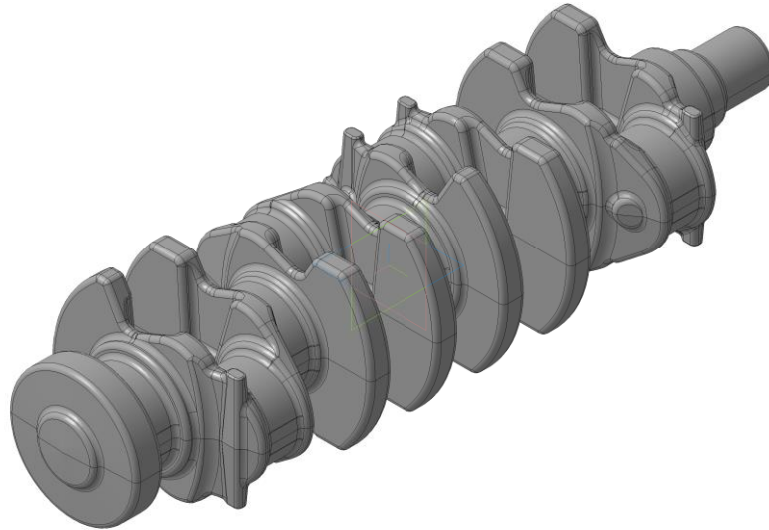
Общий вид заготовки детали - «Коленвал»
